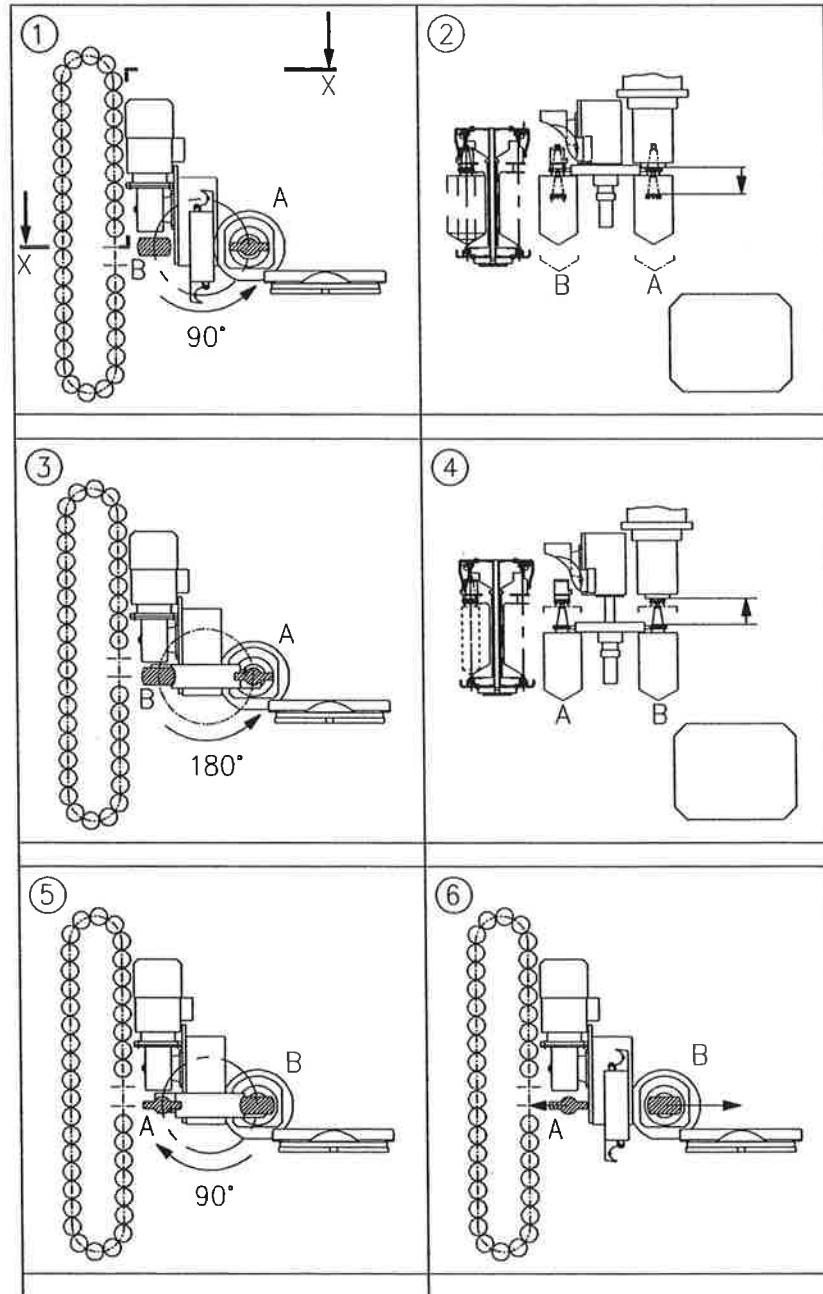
Werkzeugwechsel Ablauf
